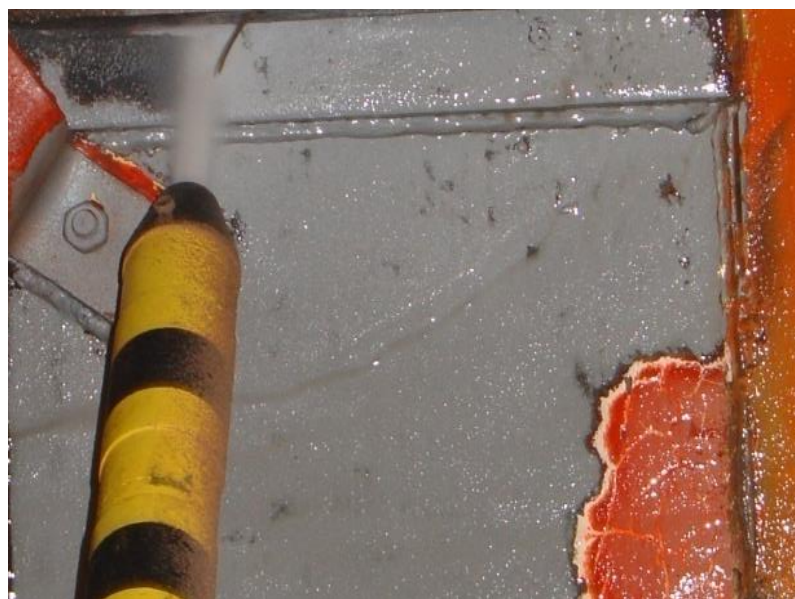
Процесс очистки поверхности детали перед нанесением лакокрасочных покрытий
